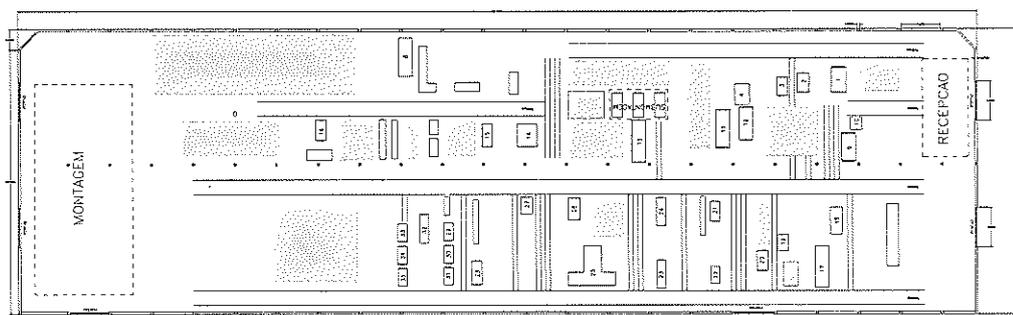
Planta da área de janelas da Pormade LTDA .
